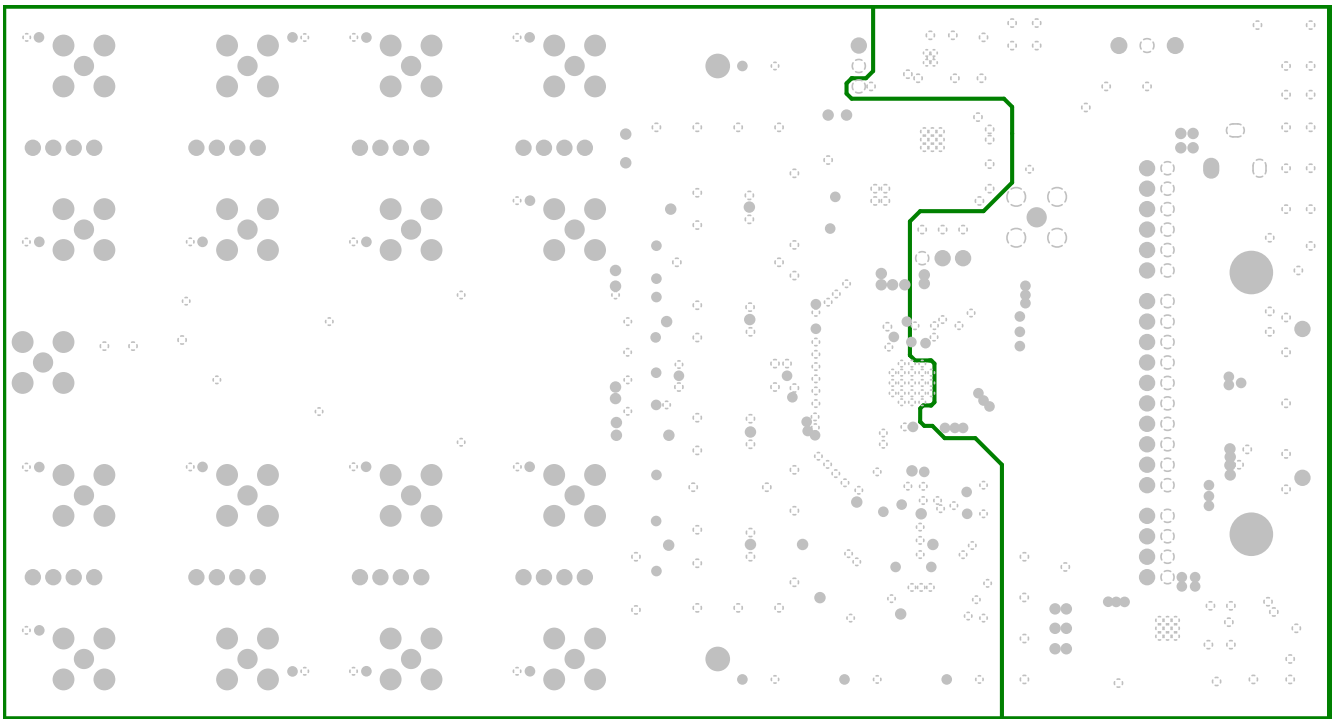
ADS127L18EVM 的 PCB 布局 (内部 AVSS/GND 平面 1)
